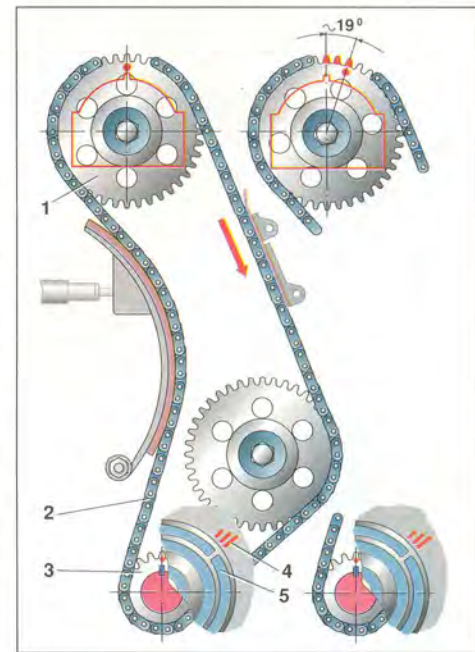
Ошибка в установке фаз газораспределения: а – нормальная регулировка; б – ошибка на два и более зубьев в сторону опережения; 1 – звездочка распредвала; 2 – цепь; 3 – звездочка коленвала; 4 – метка на передней крышке двигателя; 5 – шкив привода клиноременной передачи.
